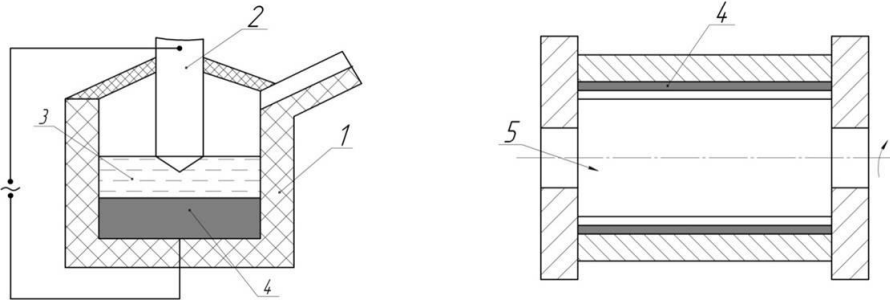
Схема електрошлакового тигельного плавлення з заливанням металу в обертову форму: 1 – тигель; 2 – електрод; 3 – шлак; 4 – розплав; 5 – заливання розплаву
